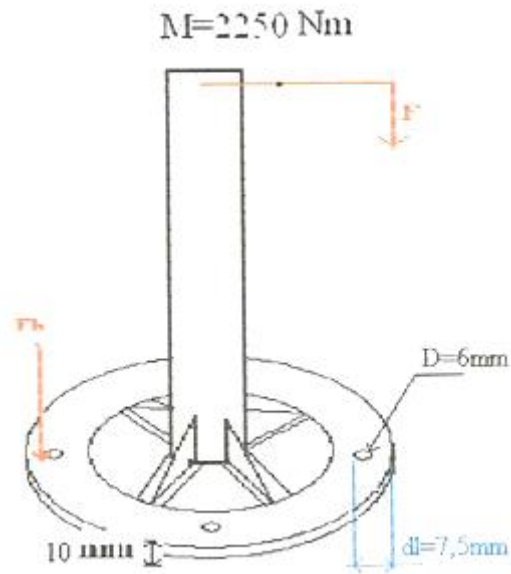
forces des boulons du poteau tubulaire supportant toute la machine.
